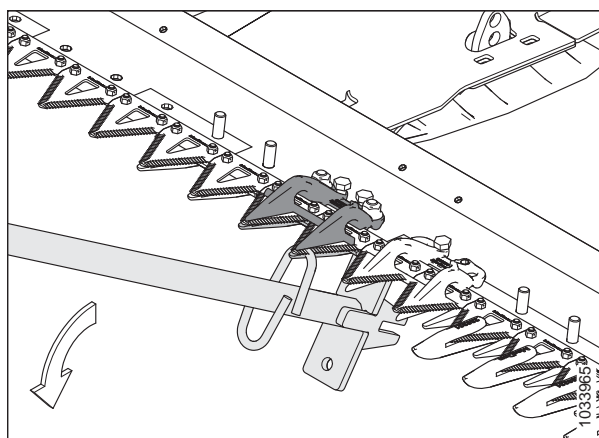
Регулировка смещением вниз — укороченный противорежущий палец
